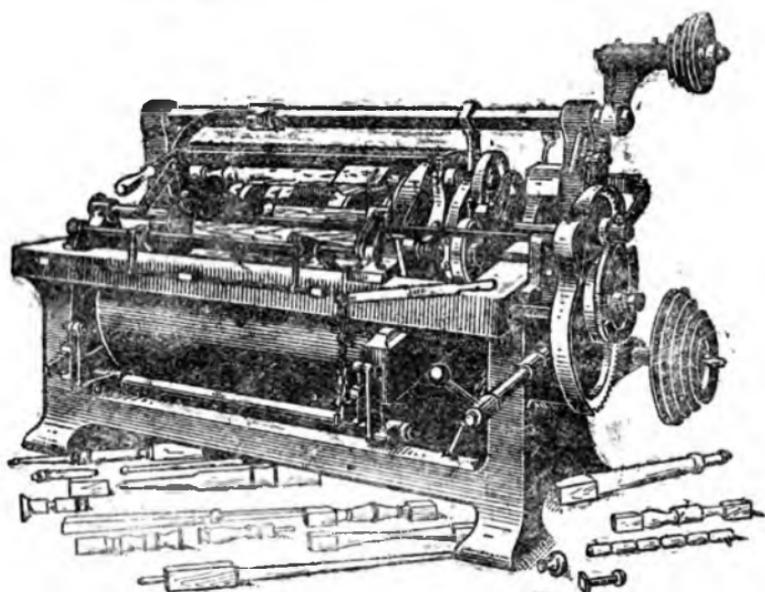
Карусельный токарно-копировально-фрезерный станок
